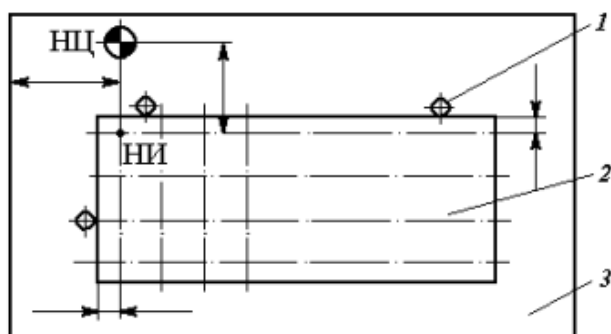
Схема расположения заготовки на столе ЛТУ: 1 – опора; 2 – заготовка; 3 – рабочий стол
